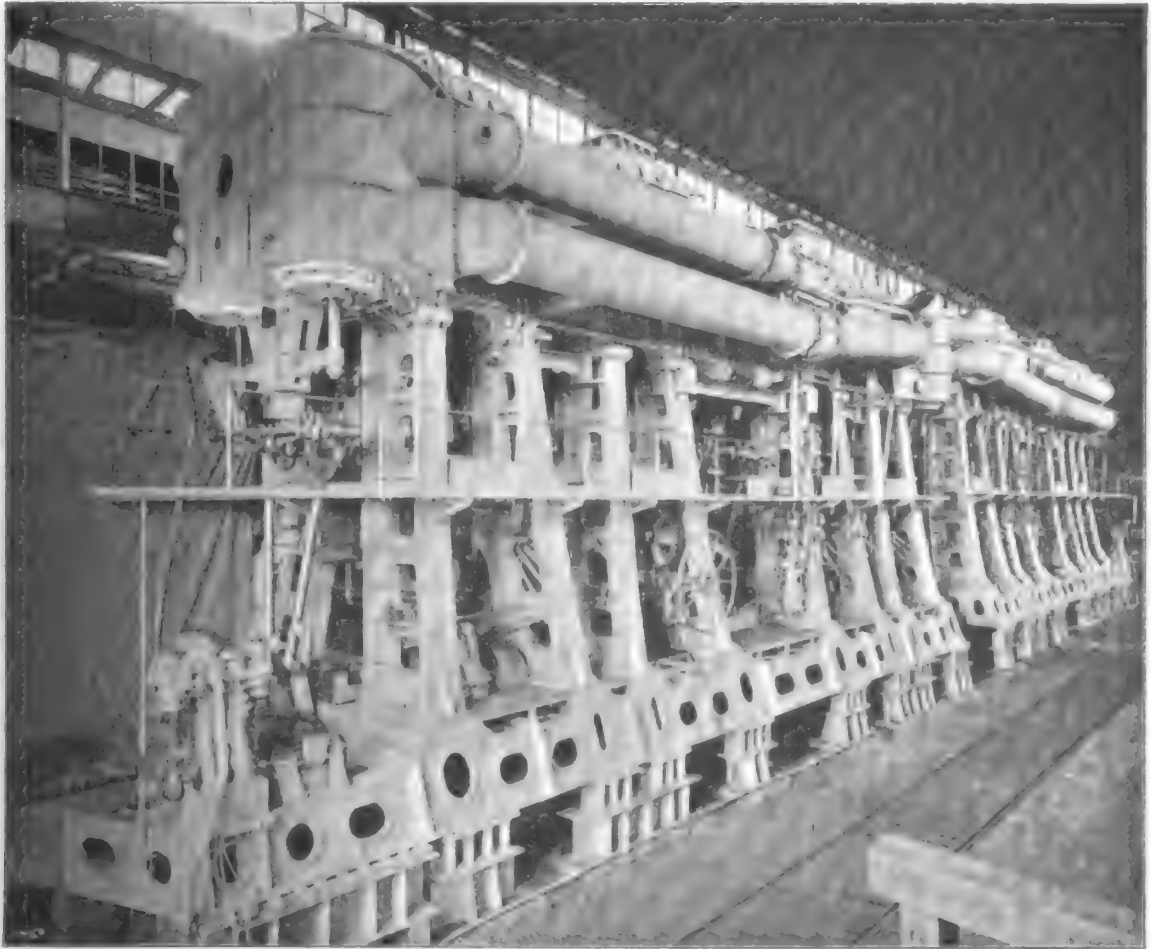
SECHSCYLINDRIGE VIERFACH-EXPANSIONSMASCHINE FÜR DEN SCHNELLDAMPFER „DEUTSCHLAND“.
